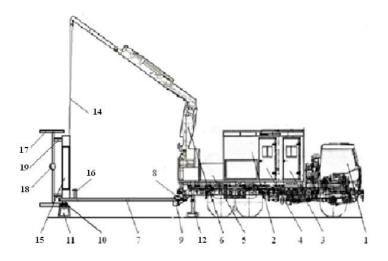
Установка подразобранного автомобиля на разборную конструкцию:
